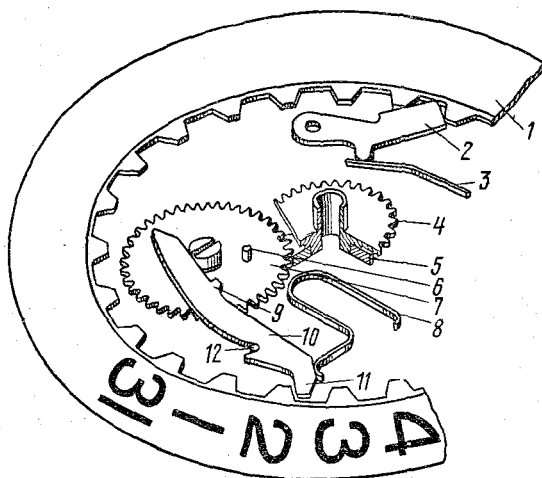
Кинематическая схема календарного устройства мгновенного действия:
